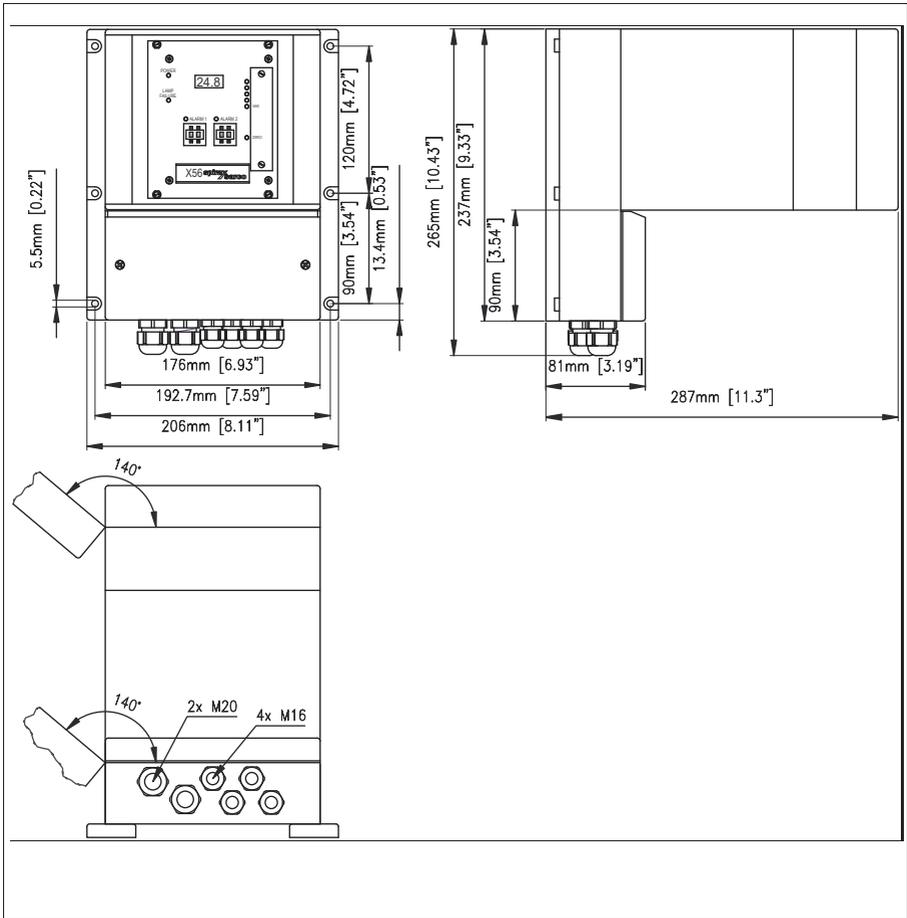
Dimensiones para la Caja B19-21 de montaje en pared.
